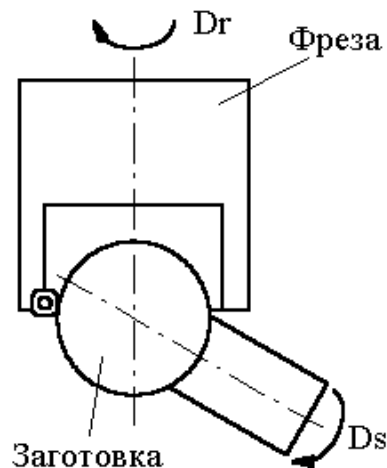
Схема обработки сферической поверхности фрезерованием.
